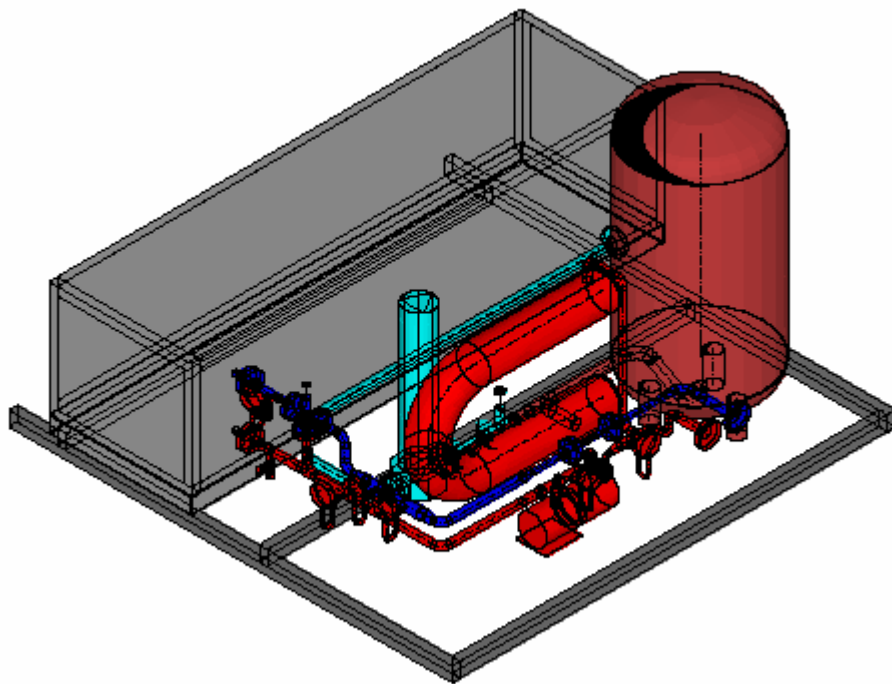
3D-Zeichnung der Pumpengruppe mit Rückkühler
